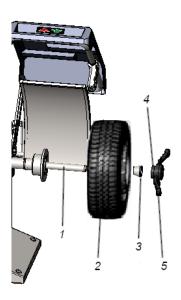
Установка колёс, конус снаружи 1 — вал резьбовой, 2 — колесо, 3 — конус, 4 — упорное кольцо, 5 — быстросъёмная гайка
